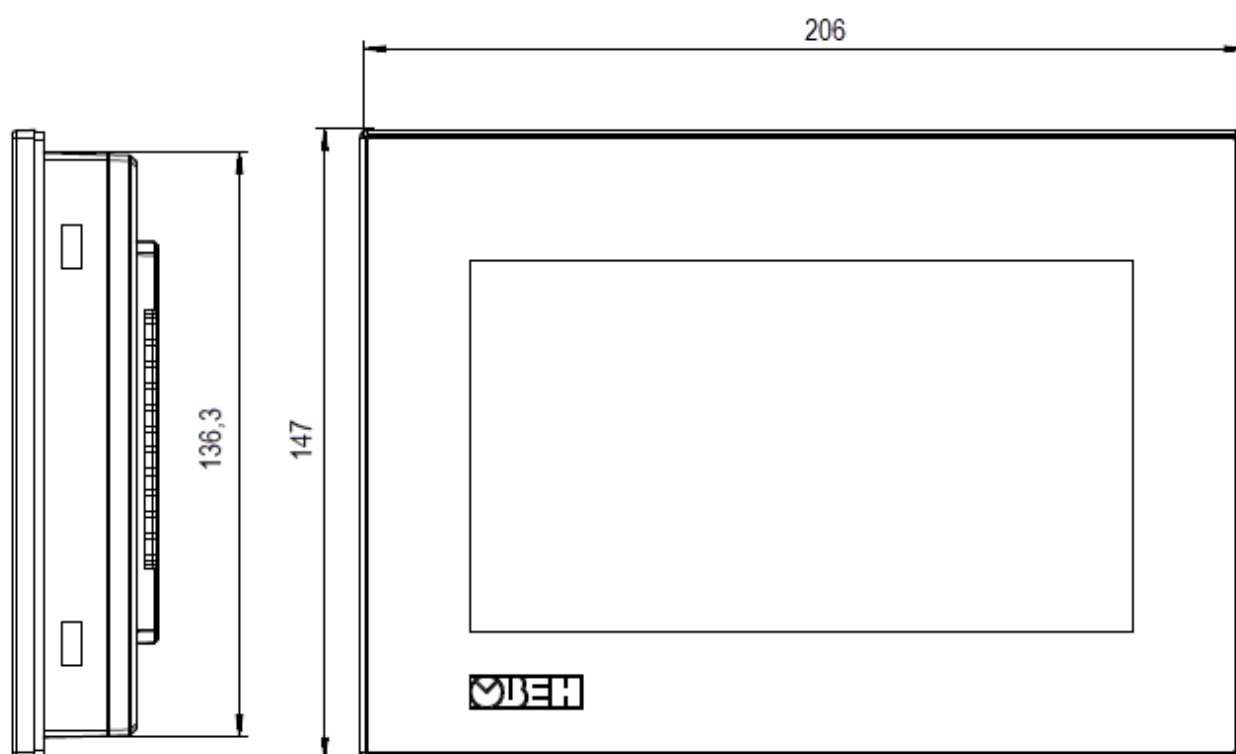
Габаритные размеры СП210-07-Б
